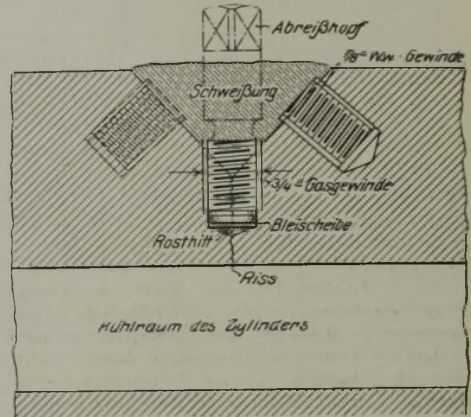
Schweißstelle eines Großgasmaschinen-Zylinders.
